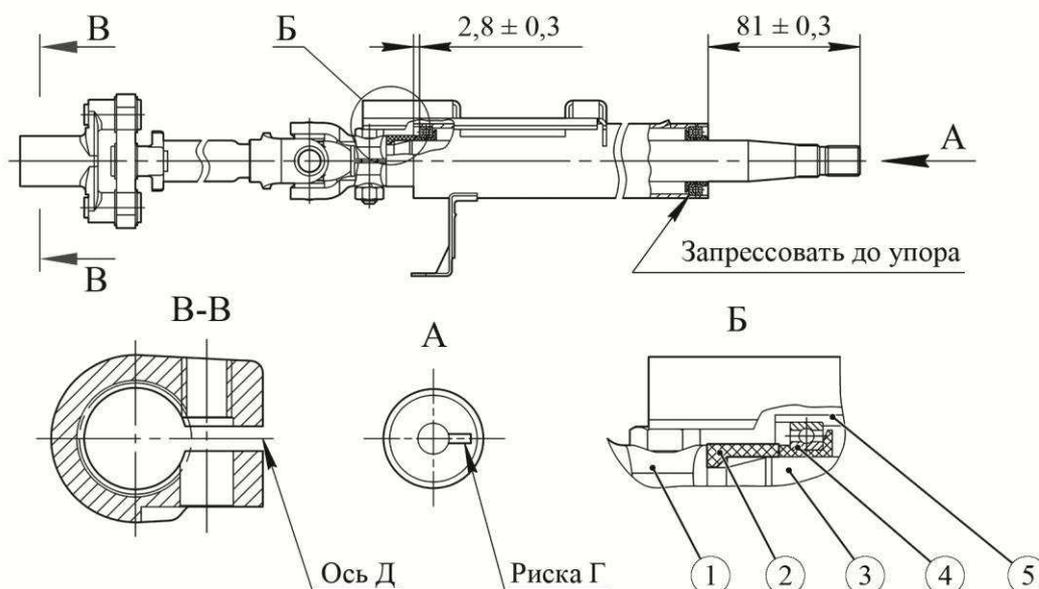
Сборка рулевого вала (обеспечить основные размеры и взаимное расположение деталей в узле):
